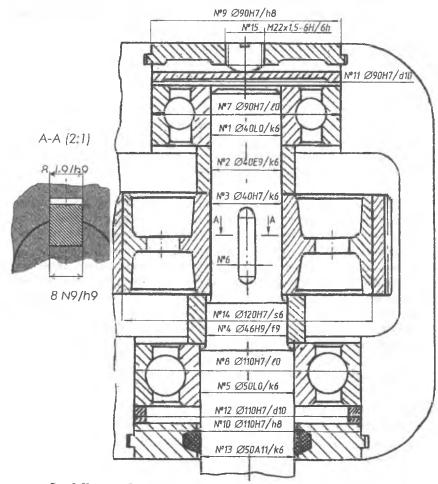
Чертёж сборочной единицы двухступенчатого редуктора
